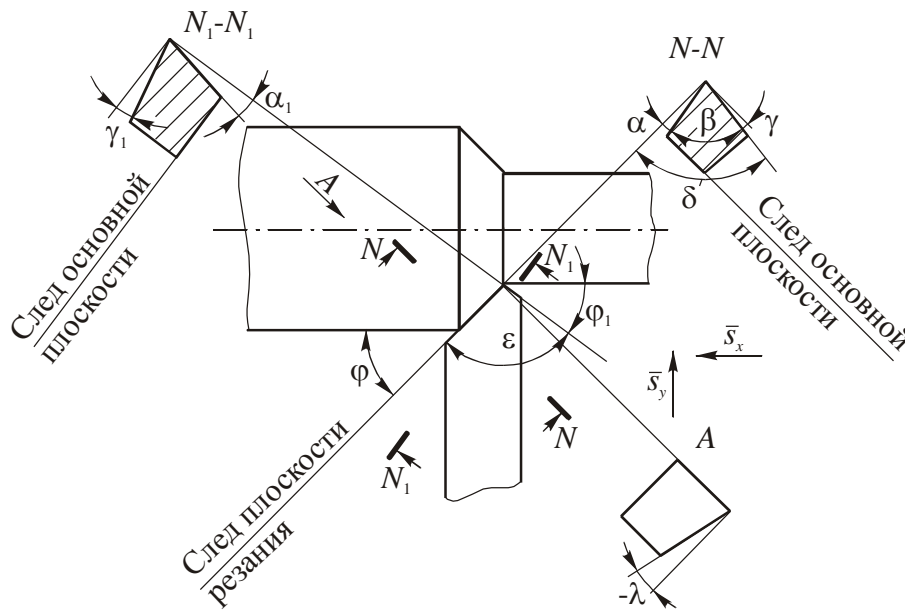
Геометрические параметры режущей части токарного проходного резца
